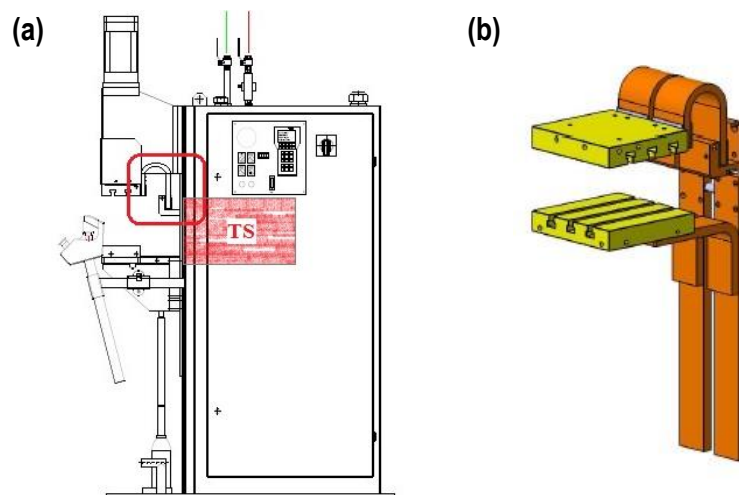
a) Ubicación de los elementos de conexión del secundario y del transformador de soldadura; y b) detalle del conexionado secundario.
